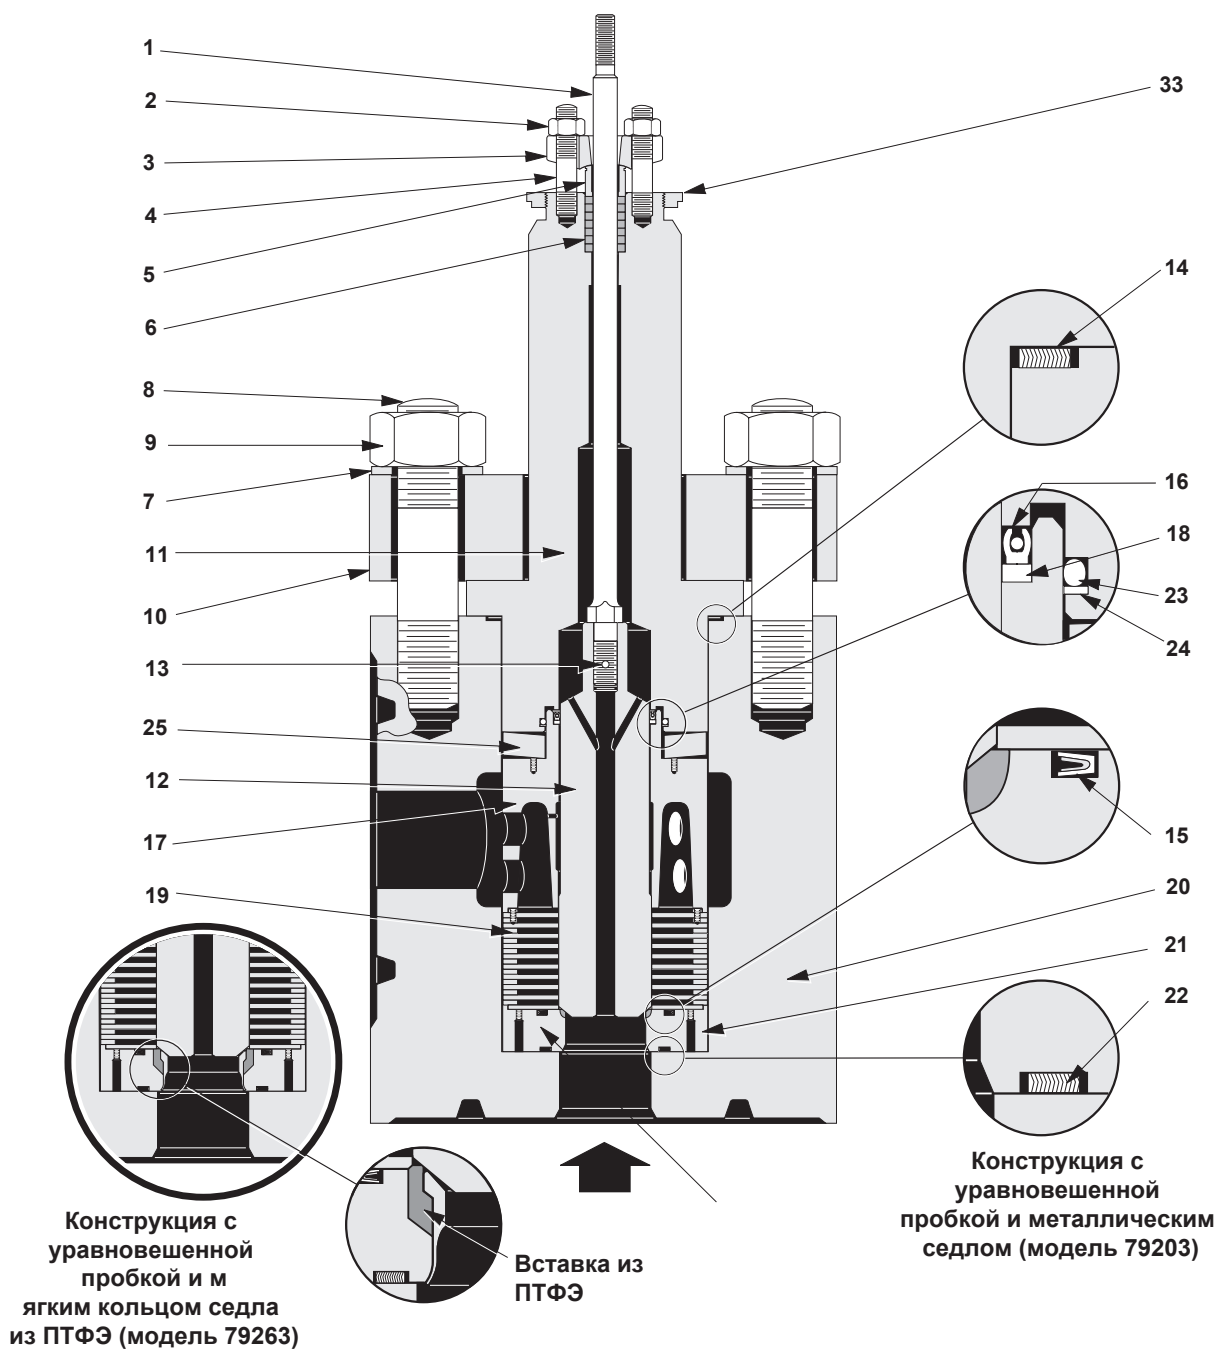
Поперечное сечение клапана VRT серии 79000 размером 3, 4 и 6 дюйма с кованным блочным корпусом
